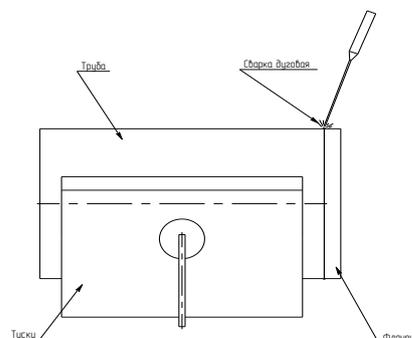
Соединение трубы и фланца сваркой
